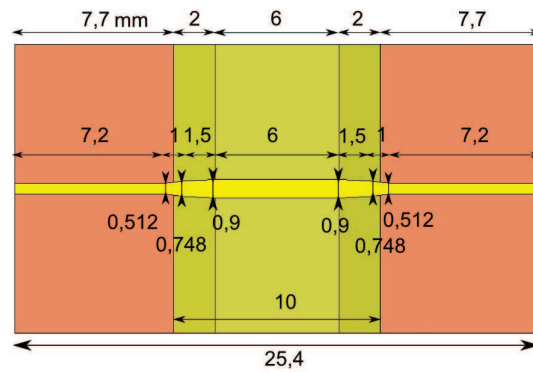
Vue du dessus et dimensions (mm) des éléments du déphaseur
